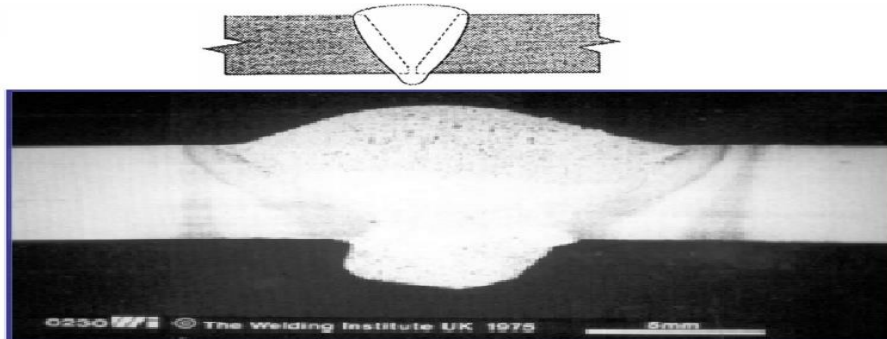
Radiografía soldadura con exceso de penetración.
